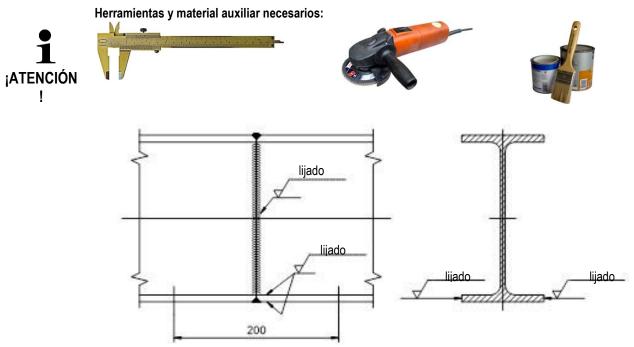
Desgaste de los soportes del perfil de rodadura soldados
